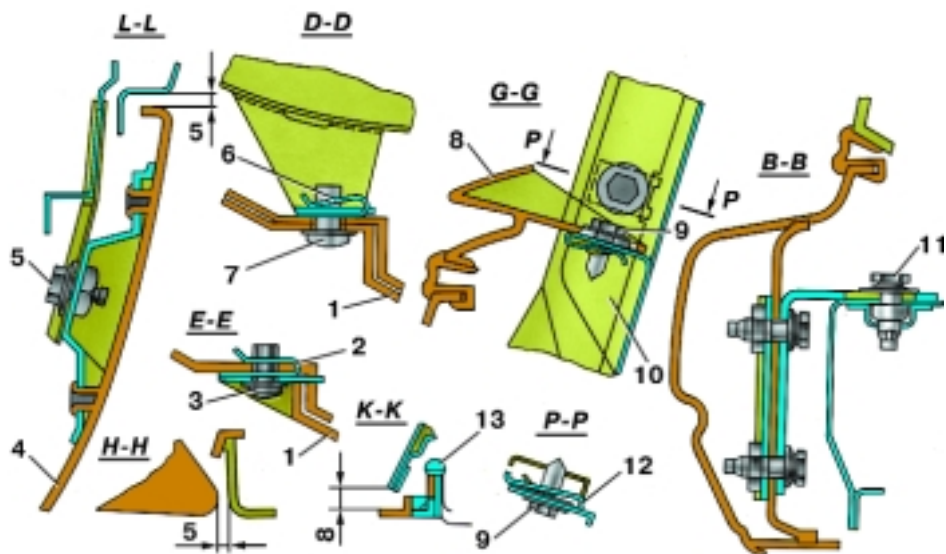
Установка облицовки радиатора и переднего буфера: 1 – поддон буфера; 2 – пластинчатая гайка; 3 – винт крепления поддона; 4 – передний буфер; 5, 11 – болты крепления переднего буфера; 6 – пластинчатая гайка; 7 – винт; 8 – решетка радиатора; 9 – самонарезающий винт; 10 – кронштейн крепления решетки радиатора; 12 – пластинчатая гайка; 13 – скоба
